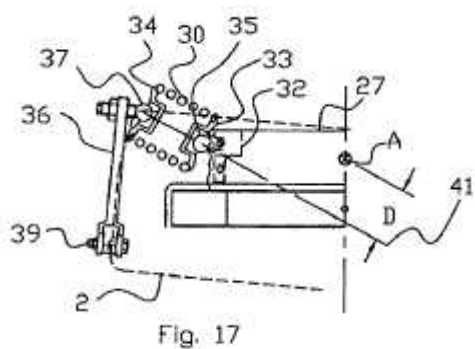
Vue en coupe à hauteur de la tête du brassard (pas collectif au maximum)
